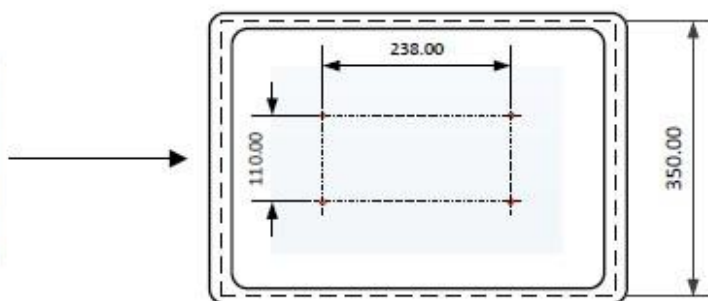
Ubicación de perforaciones para fijación de batería auxiliar
